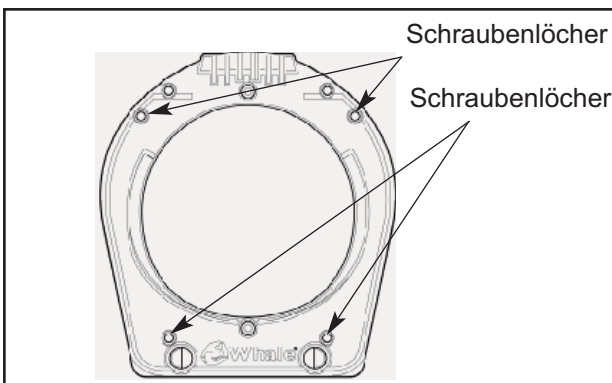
Ansicht der Befestigungspositionen ohne Hebel
